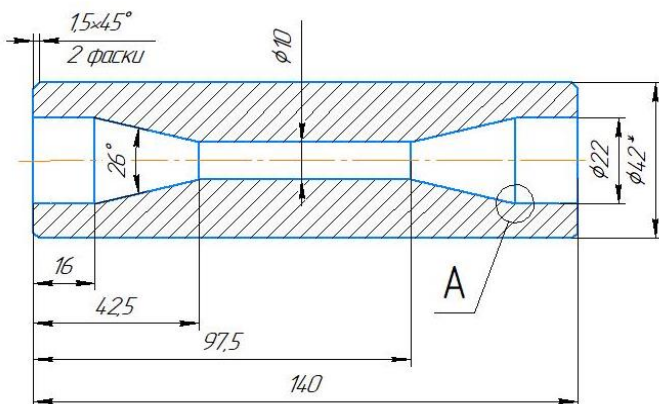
Эскиз поршневого пальца с изменённой конструкцией
